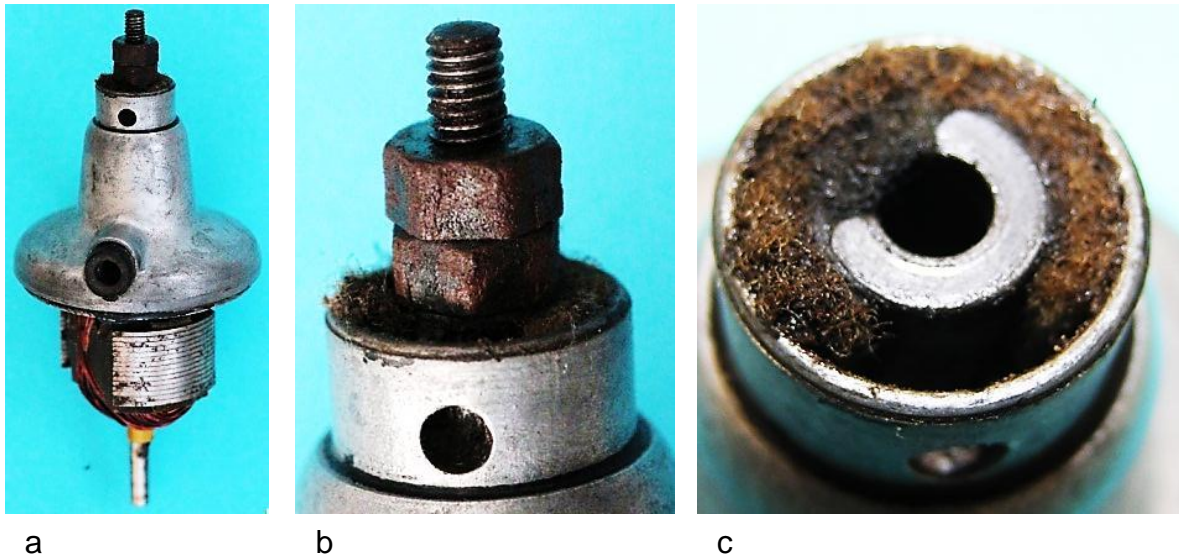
Öldepot: a) Lagerhals mit Anker, b) Lagerspieleinstellung, c) Angeschlitten-
